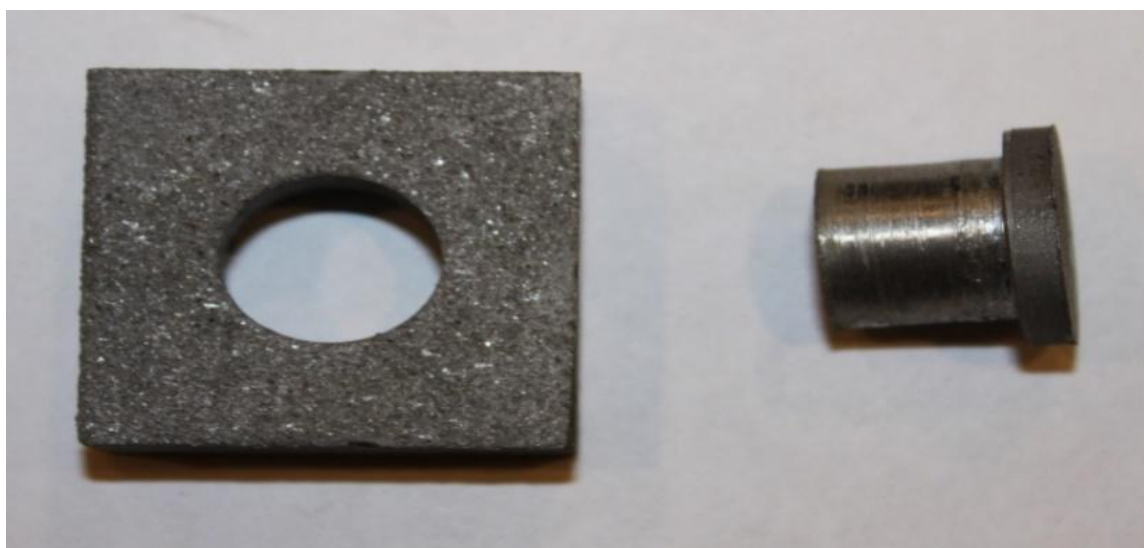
Внешний вид образца для исследования прочности сцепления покрытия и основного металла
